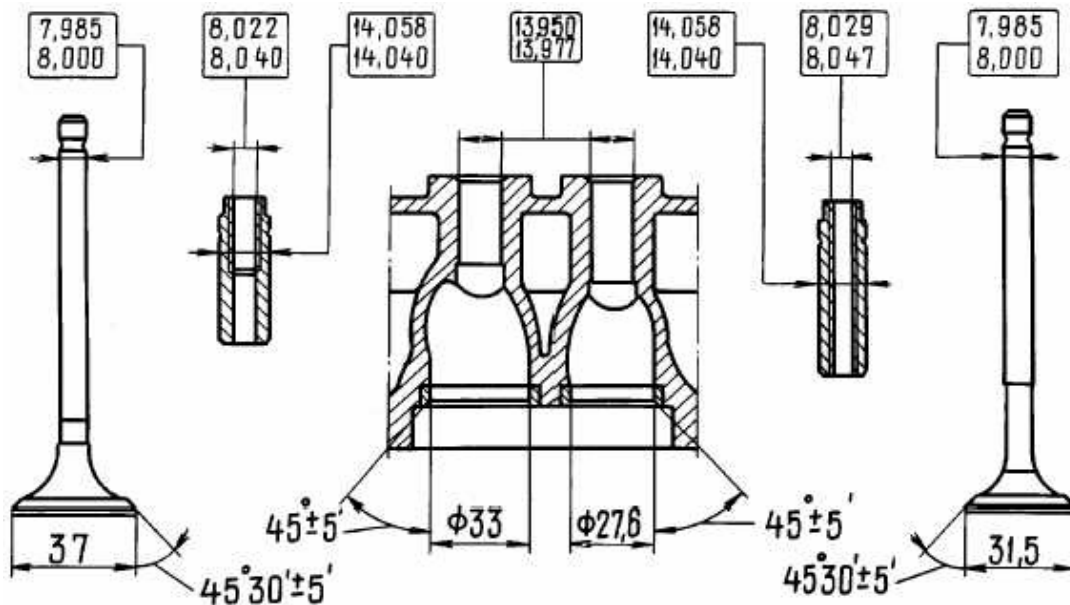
Dimensiones principales de la culata de los cilindros, válvulas y casquillos guía
